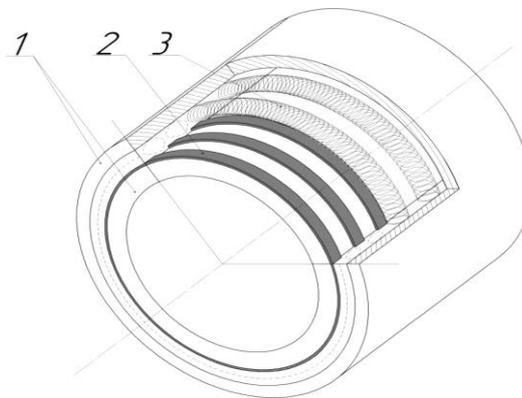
Схема вкладыша подшипника с металлическими элементами в виде ленты и пружин: 1 - слои проклеенной древесины; 2 - металлическая лента; 3 - пружина
